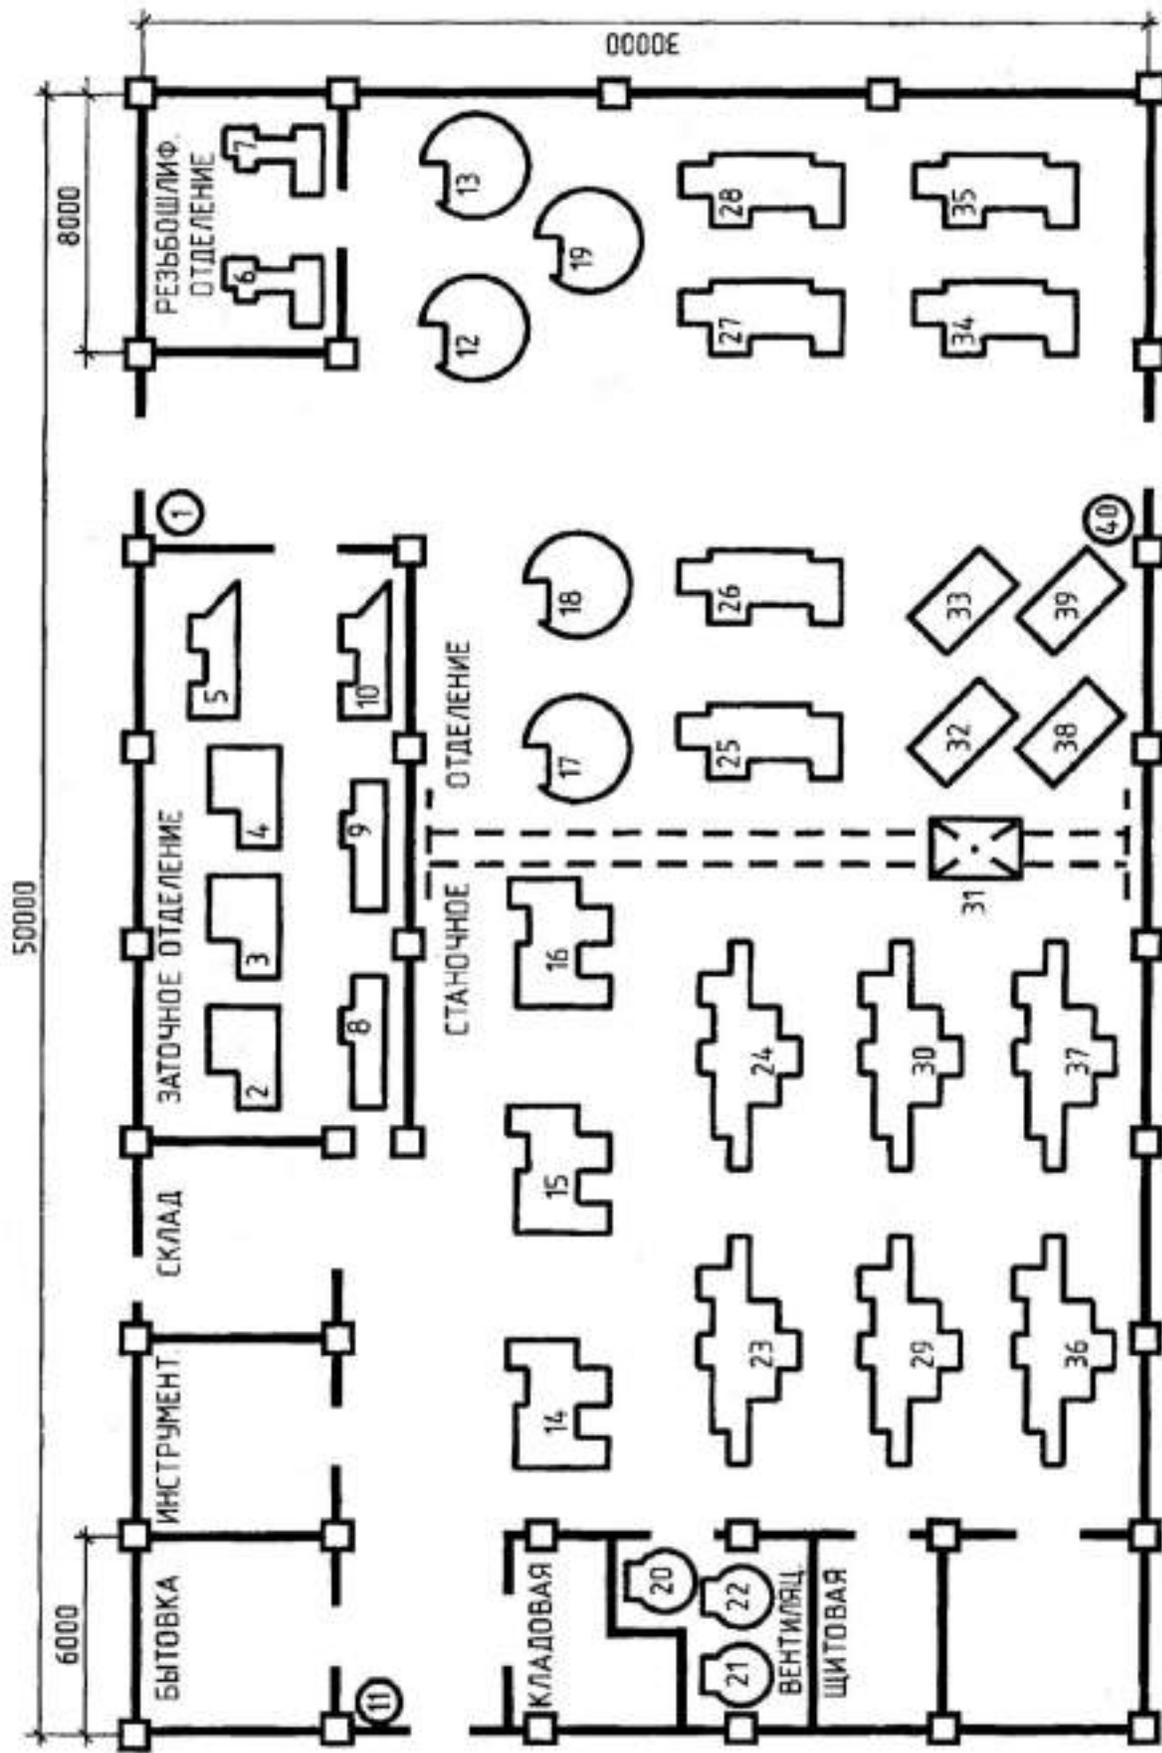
План расположения ЭО цеха металлорежущих станков
